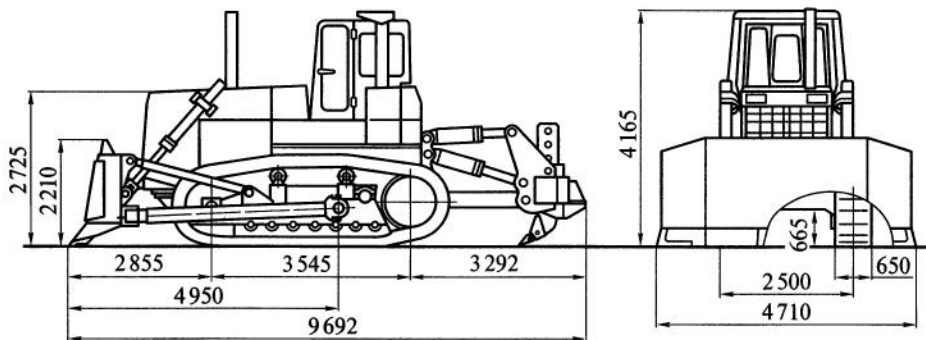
Бульдозерно-рыхлительный агрегат на базе трактора Т-35.01Я
